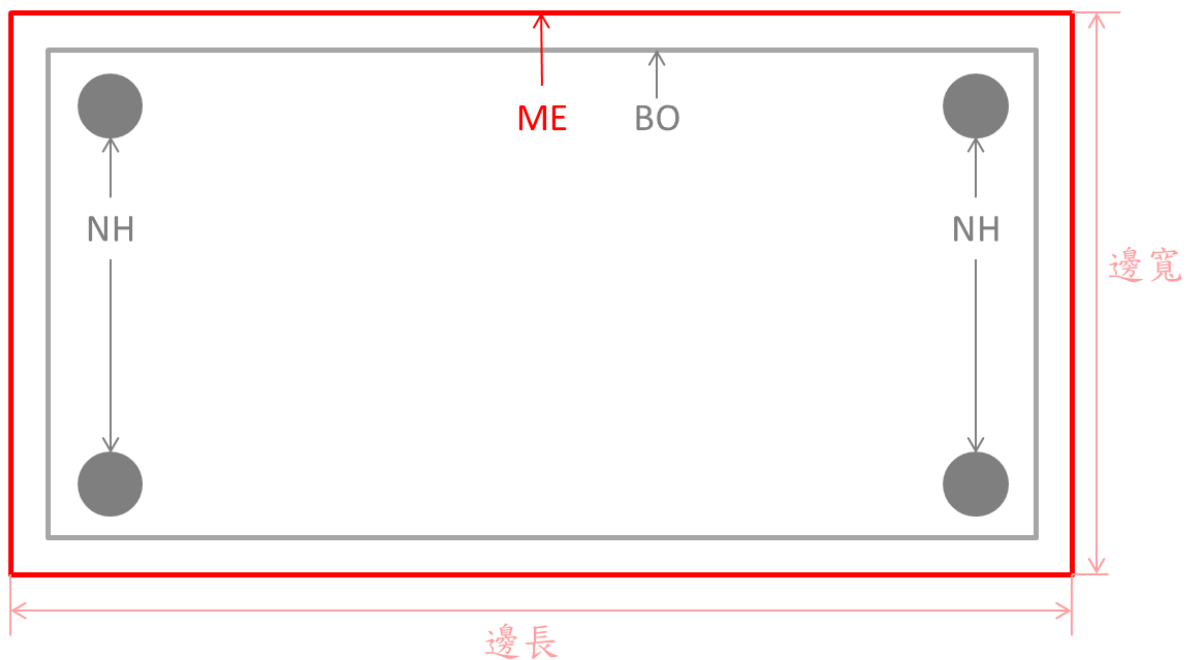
PCB 外圍邊框 ME 和板框 BO
